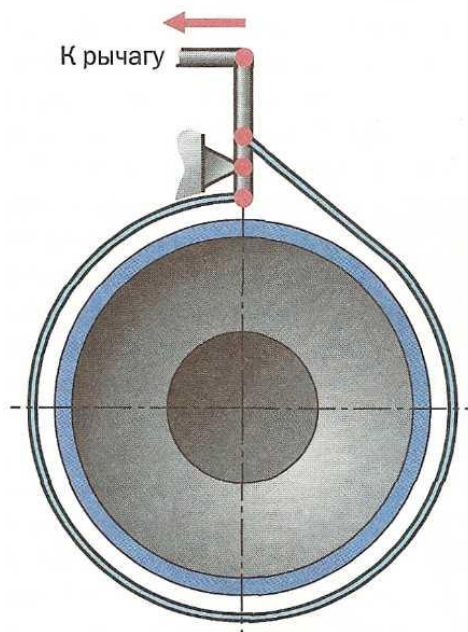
Стрічковий барабанний гальмівний механізм
